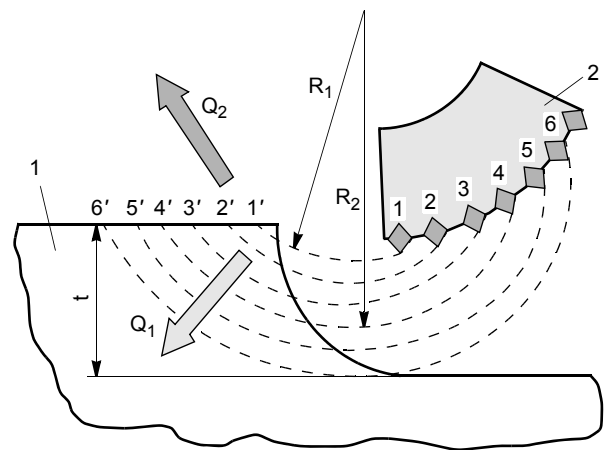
Схема послыстного удаления припуска кругом с прерывистой рабочей поверхностью: 1 — заготовка, 2 — сегмент круга
